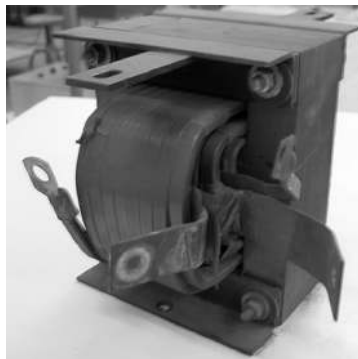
Transformador de soldadura, observar la sección del devanado secundario.
